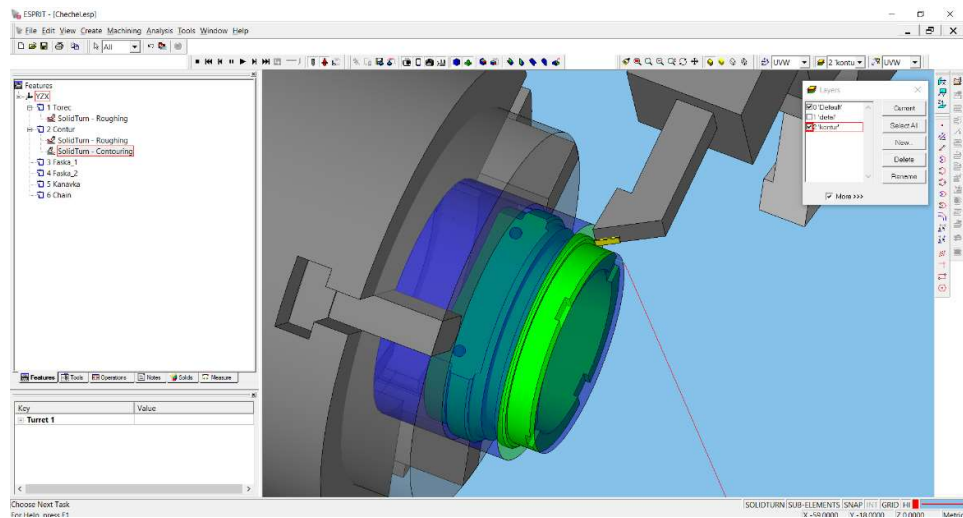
Траєкторія руху металорізального інструменту при обробленні контуру кришки
